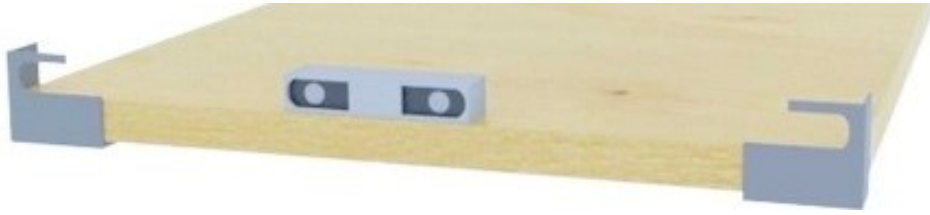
telecamera con protezione posizionata sul piano con supporti alle estremità
